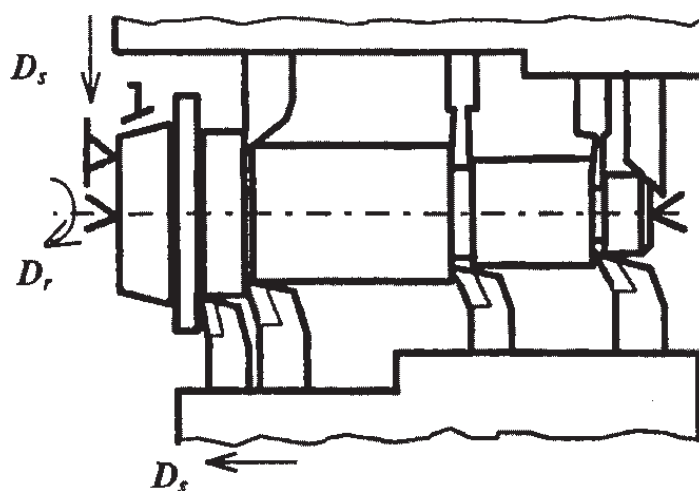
Схема обработки наружных поверхностей на многолезцовом токарном станке
